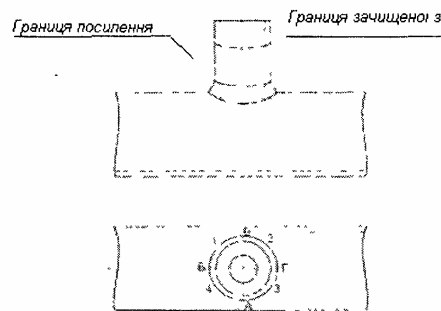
Схема розмічування углового сварного соединения на сектора
